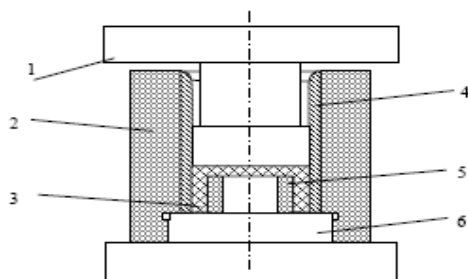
Экспериментальная прессформа для объёмной штамповки металлополимерных подшипников скольжения:
